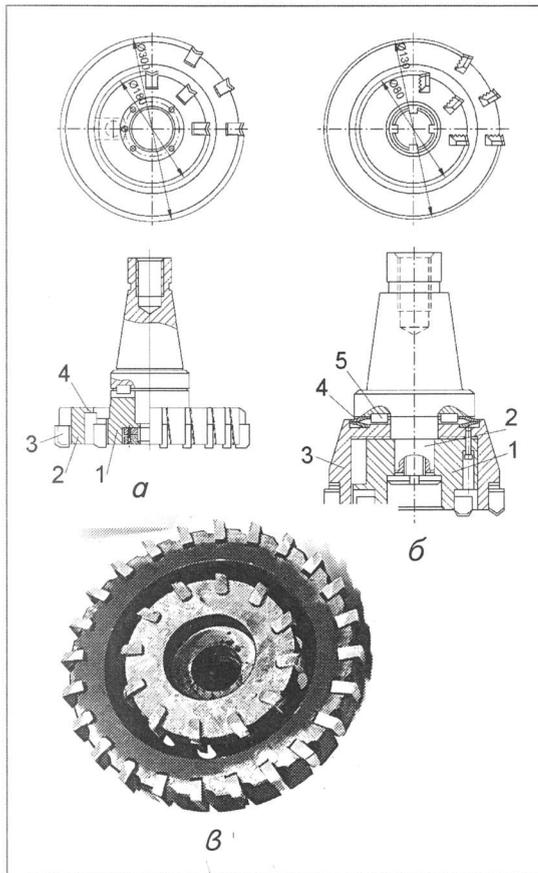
Упругодемпфированные двухрядные торцовые фрезы: а — целая, б — сборная, в — общий вид 1 и 2 — жесткий и демпфированный контуры зубьев, 3 — упругий элемент, 4 — режущий зуб).
